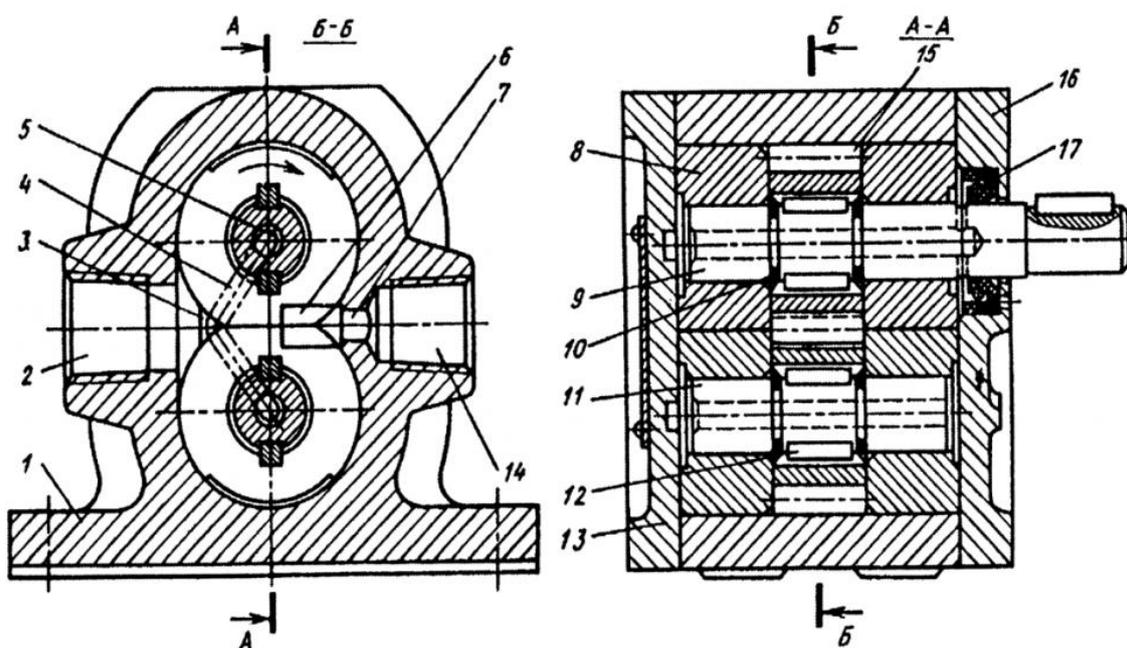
Сборочный чертеж насоса шестеренчатого Г11-22
